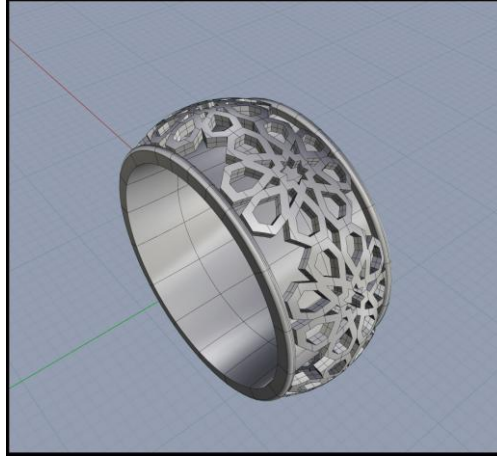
Alyansın Vray motoru ile görselleştirilmesi
